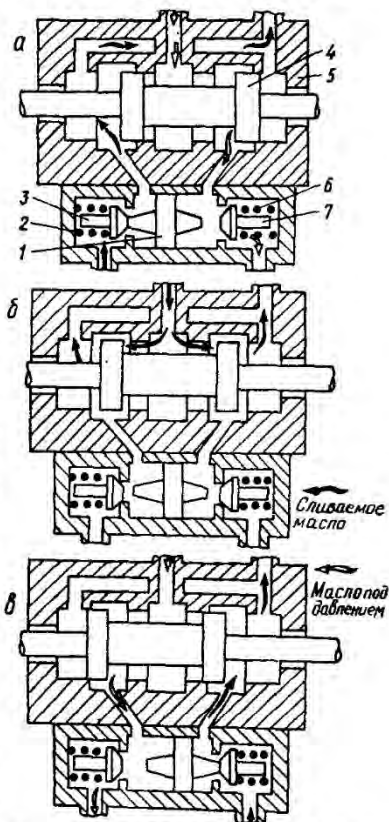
Схема положений золотника распределителя и клапанов рулевого управления трактора Т-150К:
